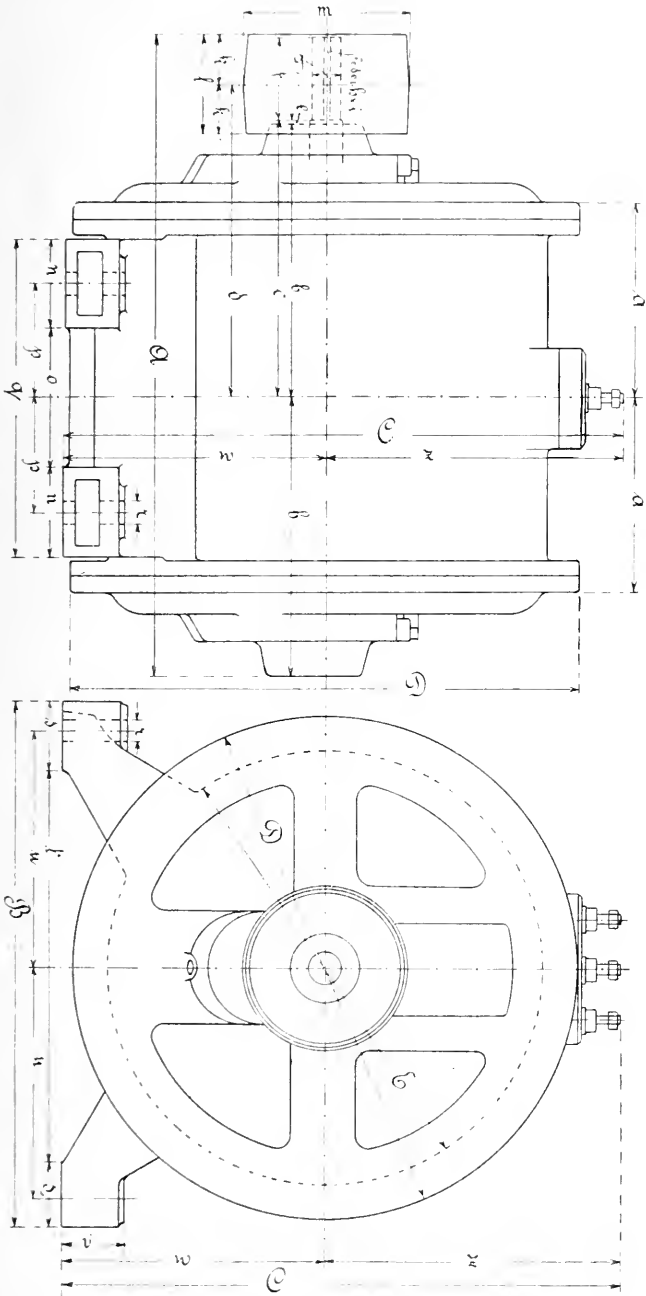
Maßzeichnung. (Drehstrommotor von Kolben & Co. Prag.)
